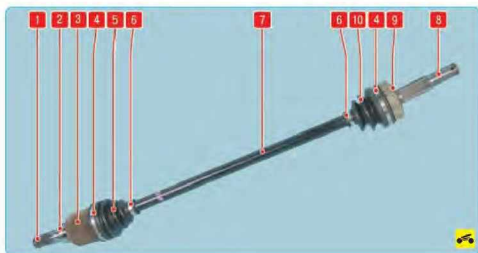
Привод заднего колеса: 1 – стопорное кольцо; 2 – пыльник сальника внутреннего шарнира; 3 – внутренний шарнир; 4 – большой хомут крепления чехла шарниров; 5 – чехол внутреннего шарнира; 6 – чехол внутреннего шарнира; 7 – вал привода заднего колеса; 8 – наружный шарнир привода заднего колеса; 9 – зубчатое кольцо датчика частоты вращения заднего колеса; 10 – чехол наружного шарнира
